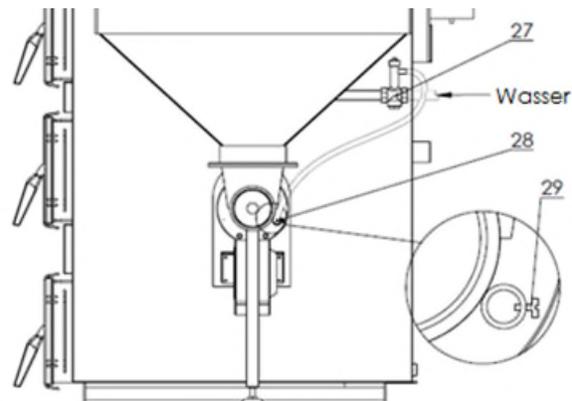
Installationsschema mit 2-Wege-Sicherheitsventil DBV1
